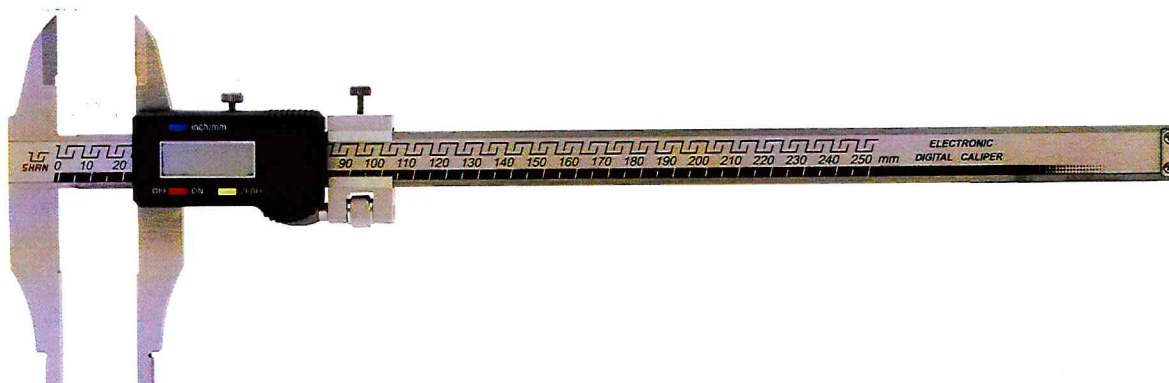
Общий вид штангенциркулей двусторонних без глубиномера с цифровым отсчетным устройством
